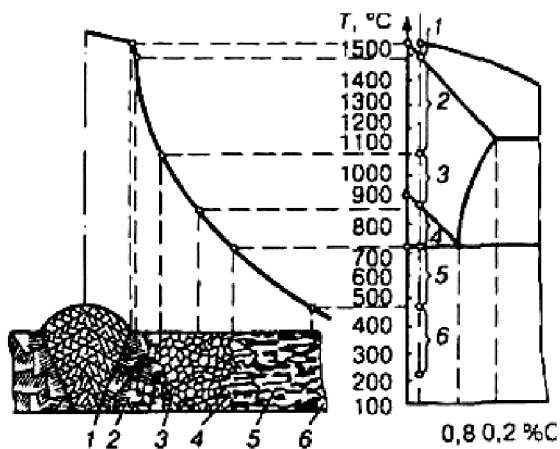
Схема будови зварного шва і зони термічного впливу
